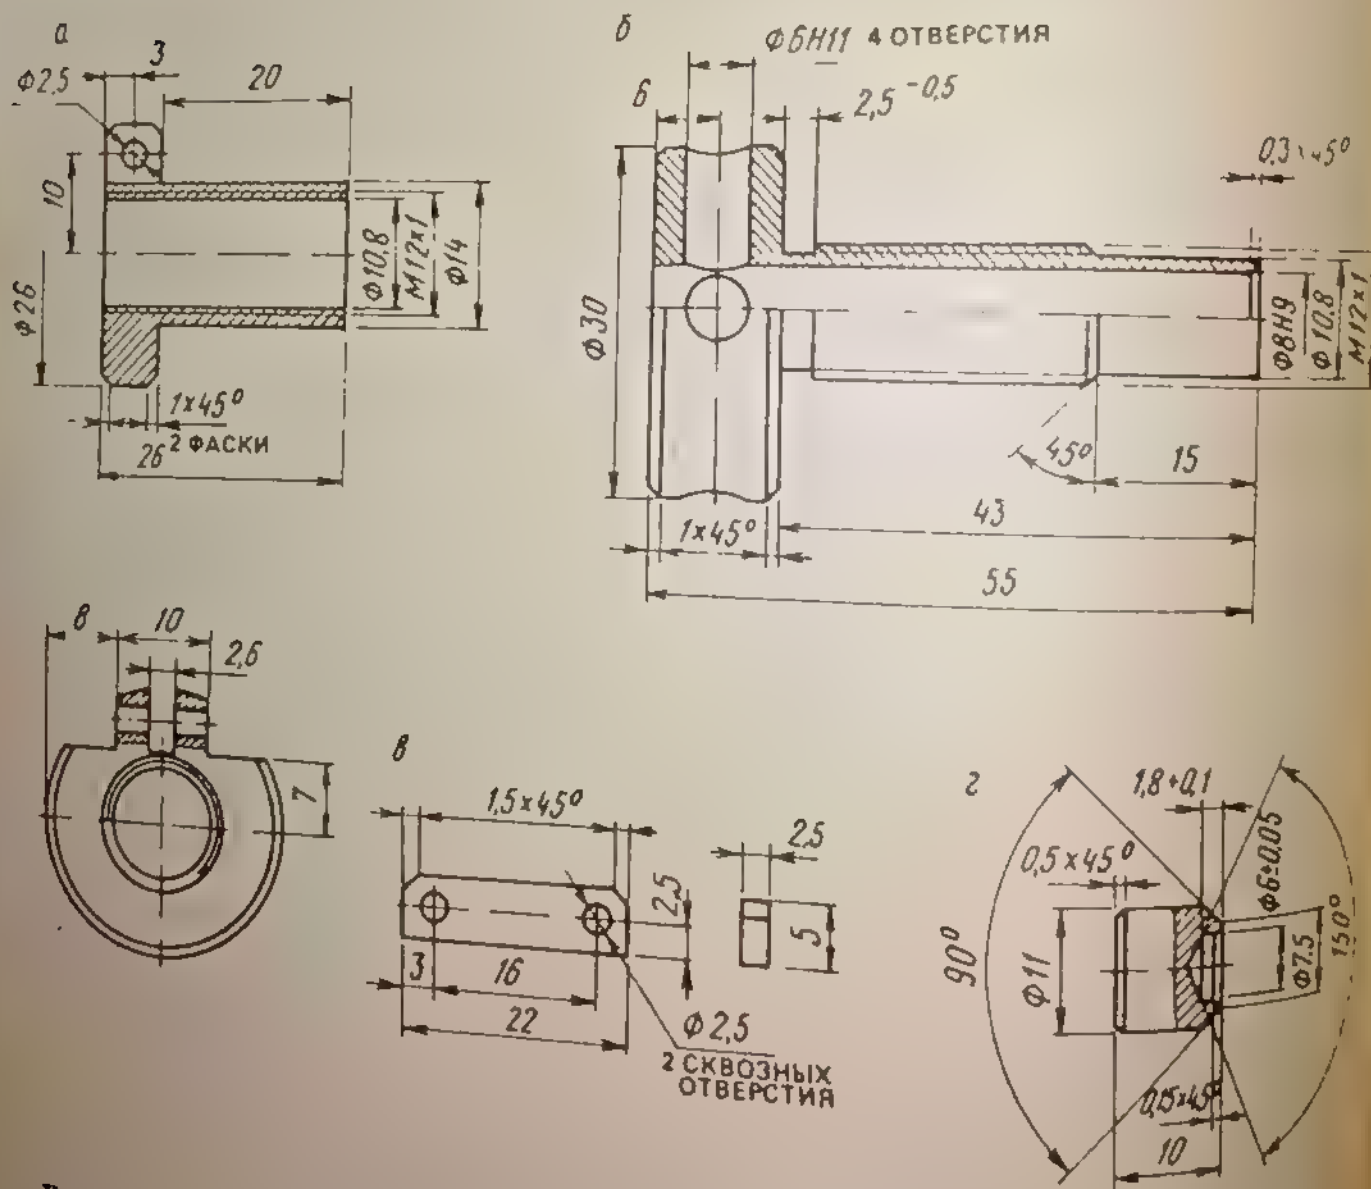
Элементы приспособления для фрезерования седла поплавкового клапана противодавления и заменяемая деталь
